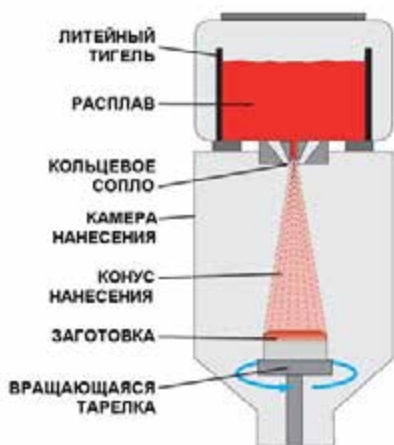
ro-35: Схематическое изображение процедуры нанесения расплавленного металла на заготовку; источник: MSI
